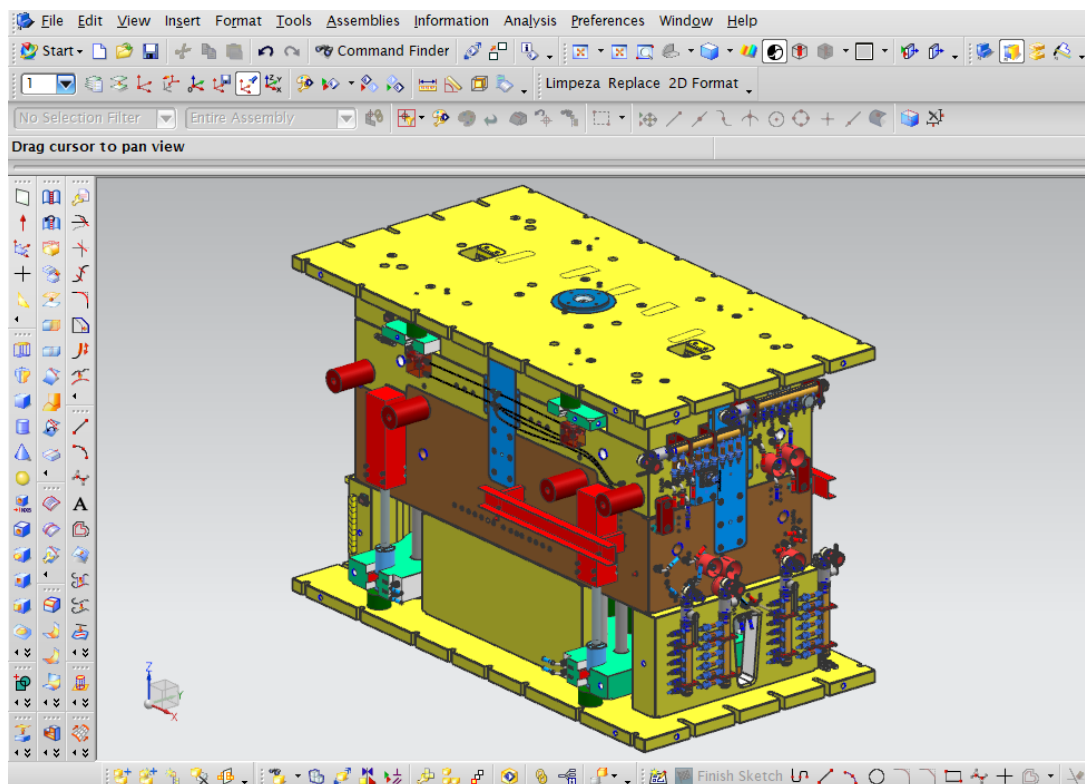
Desenho 3D de um molde para o fabrico de para-choques de automóvel [Fonte: (MoldIT, 2019)].
